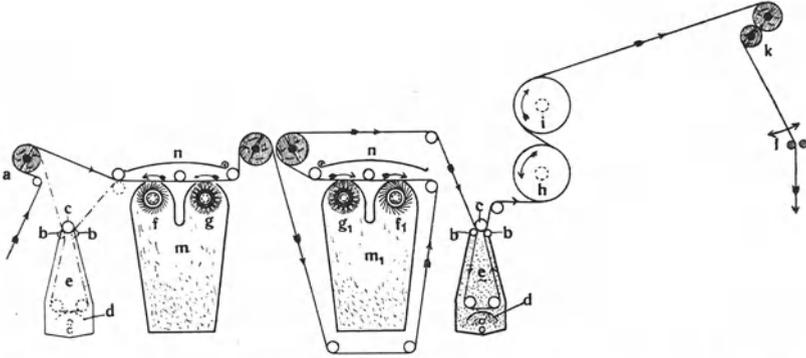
Querschnitt einer Dämpf-, Bürst- und Glättmaschine von Geßner.
